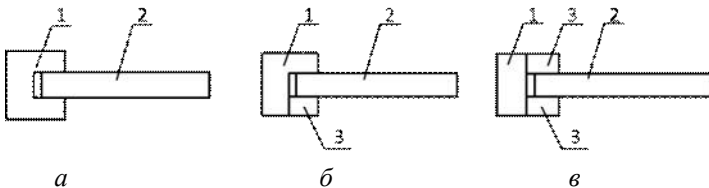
Схематичне зображення конструкції кріплення тахлі рамкових фасадів: *а*) в шпунт; *б*) в фальц; *в*) розкладками двосторонніми: 1 – брусок рамки; 2 – тахля; 3 – розкладки (штапики)
